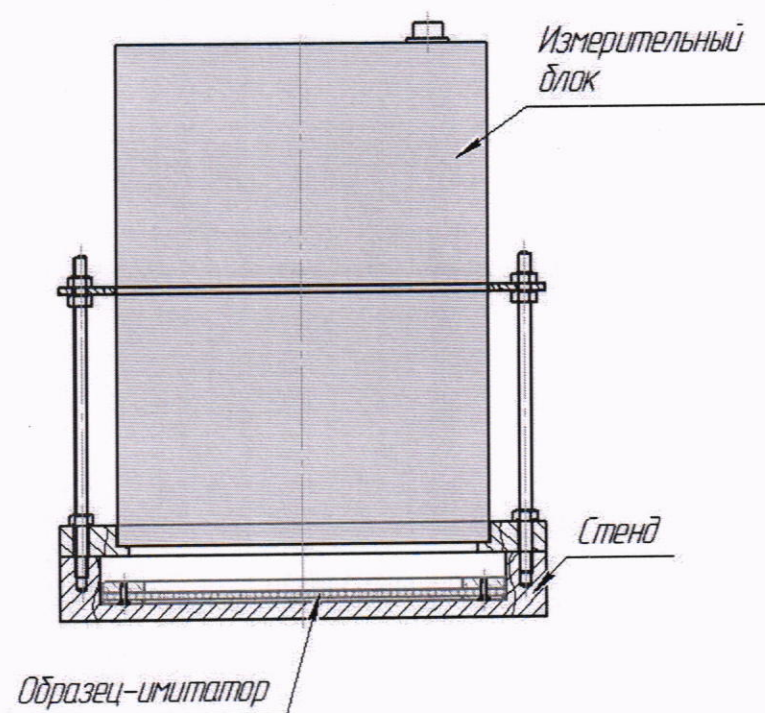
Установка толщиномера и образцов-имитаторов на стенде
